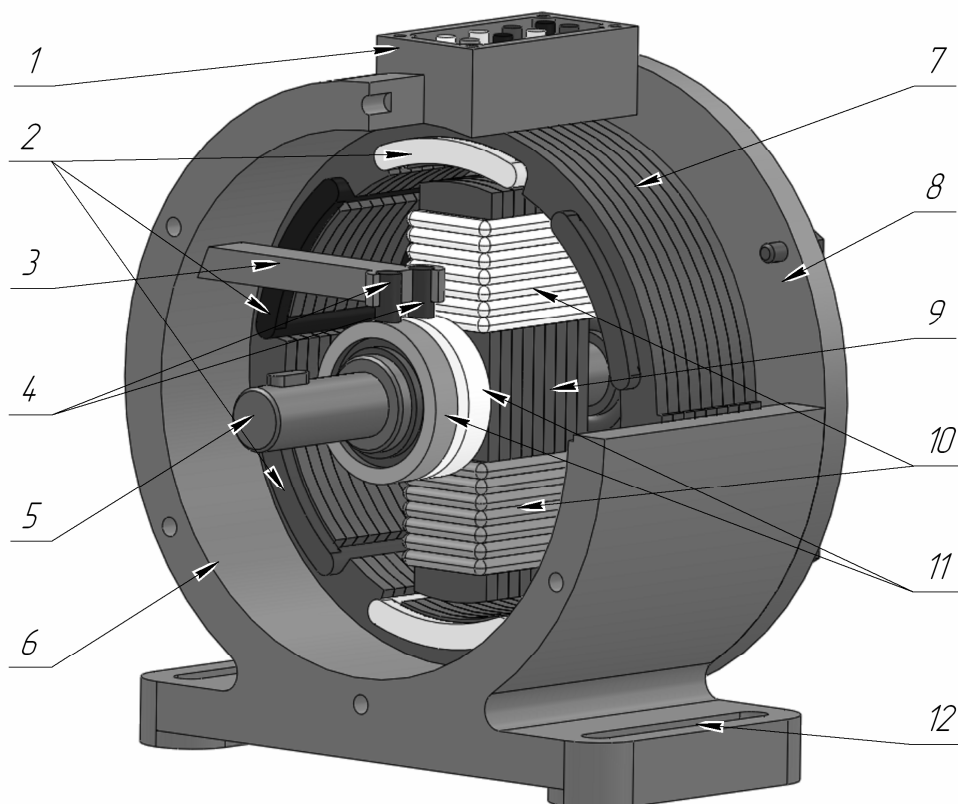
Конструкция синхронной машины: 1 – клеммник; 2 – трехфазная обмотка статора; 3 – щеткодержатель; 4 – графитовые щетки; 5 – вал; 6 – корпус; 7 – магнитопровод статора; 8 – крышка с подшипниковым узлом; 9 – магнитопровод ротора; 10 – полюсная обмотка ротора; 11 – контактные кольца; 12 – монтажные отверстия корпуса
